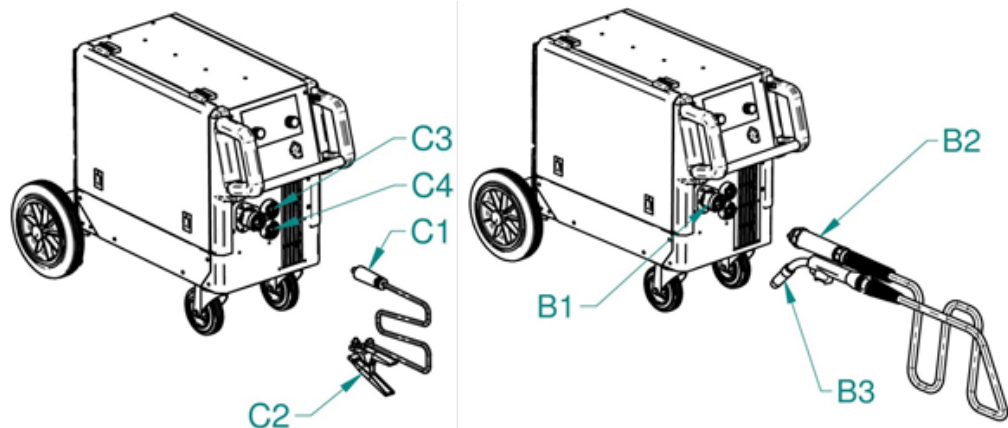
Подключение сварочной горелки и кабеля массы (показан Fanmig компактный 3200i).
